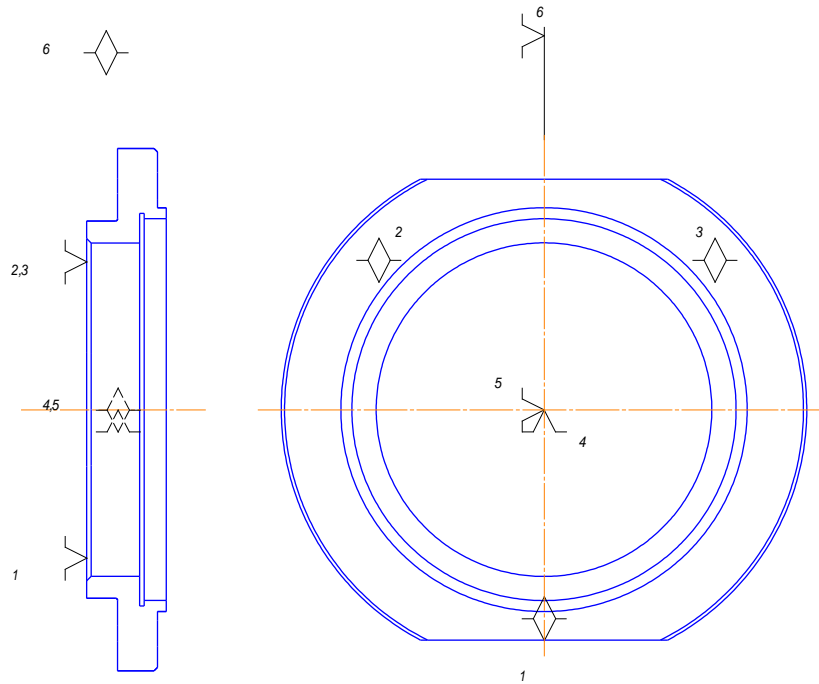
Схема базування деталі «Фланець» при механічній обробці: 1, 2, 3 – установча база А (торцева поверхня); 4, 5 – подвійна опорна база Б (зовнішня циліндрична поверхня); 6 – упорна база В, що забезпечує остаточну фіксацію заготовки.
